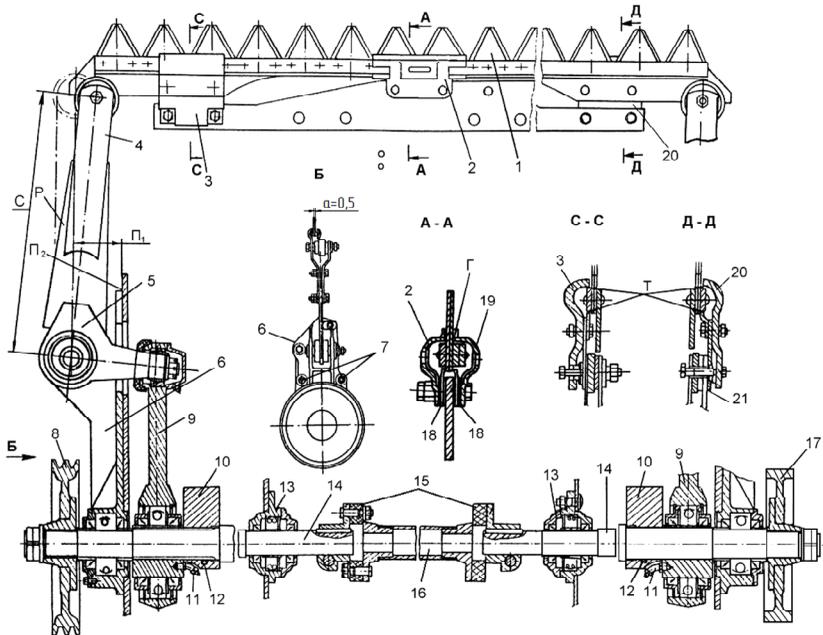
Схема регулировки беспальцевого режущего аппарата жатки для трав:
